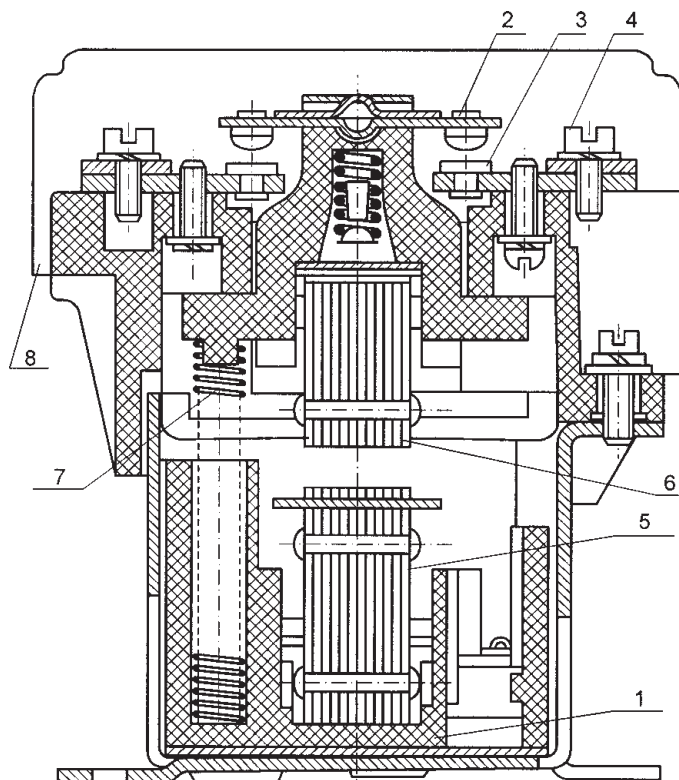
Устройство магнитного пускателя ПМЕ: 1 — основание; 2 — подвижный контактный мост; 3 — неподвижный контакт; 4 — присоединительный зажим; 5 — сердечник; 6 — якорь; 7 — возвратная пружина; 8 — дугогасительная камера
